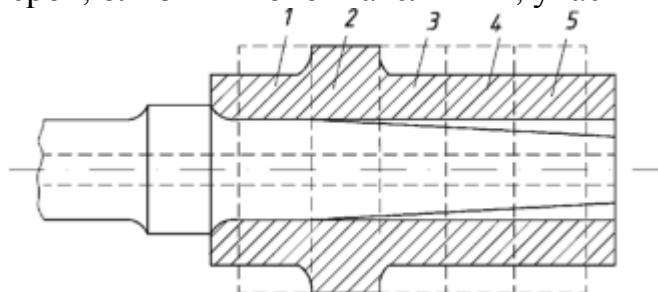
Деление заготовки на участки при протяжке полой заготовки
